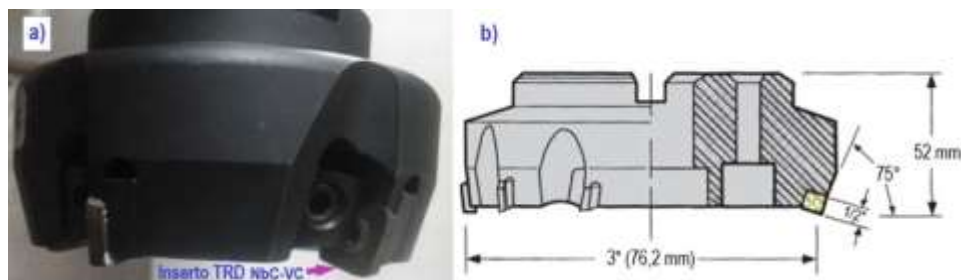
Porta insertos para maquinado: a) puesta de insertos de corte con recubrimientos NbC-VC y b) dimensiones de fresa planeadora ref. FP-3-I.[105]
